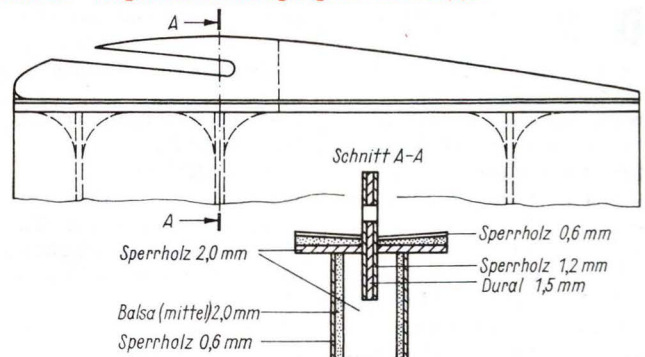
Tragflächenbefestigung mit einer Aussparung in der Mittelrippe
